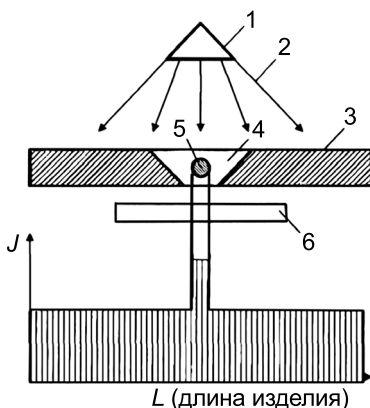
Схема просвечивания сварного соединения:
